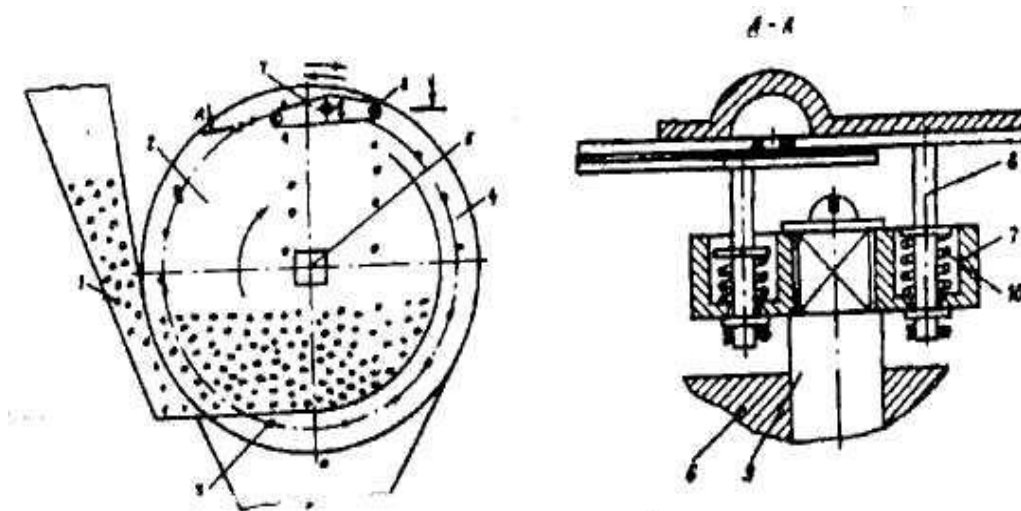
Апарат з новим виловним відбивачем: 1 - камера з насінням; 2 - висівний диск; 3 - наскрізні отвори диска, які розташовані по колу 4; 5 - вал; 6 - корпус; 7 - виловний відбивач; 8 - зуби відбивача; 9 - поворотна вісь відбивача; 10 - пружини
